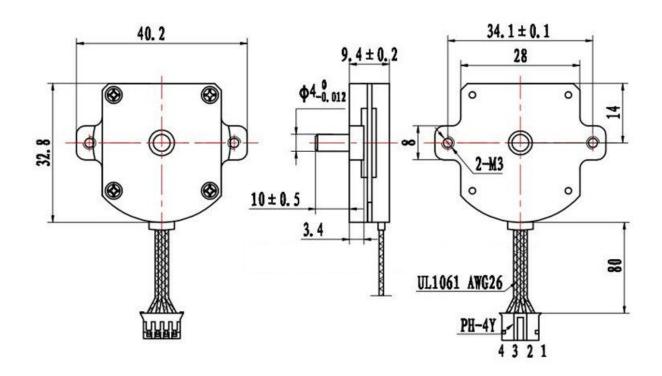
Габаритные размеры шаговых двигателей серии 28BYGH10
